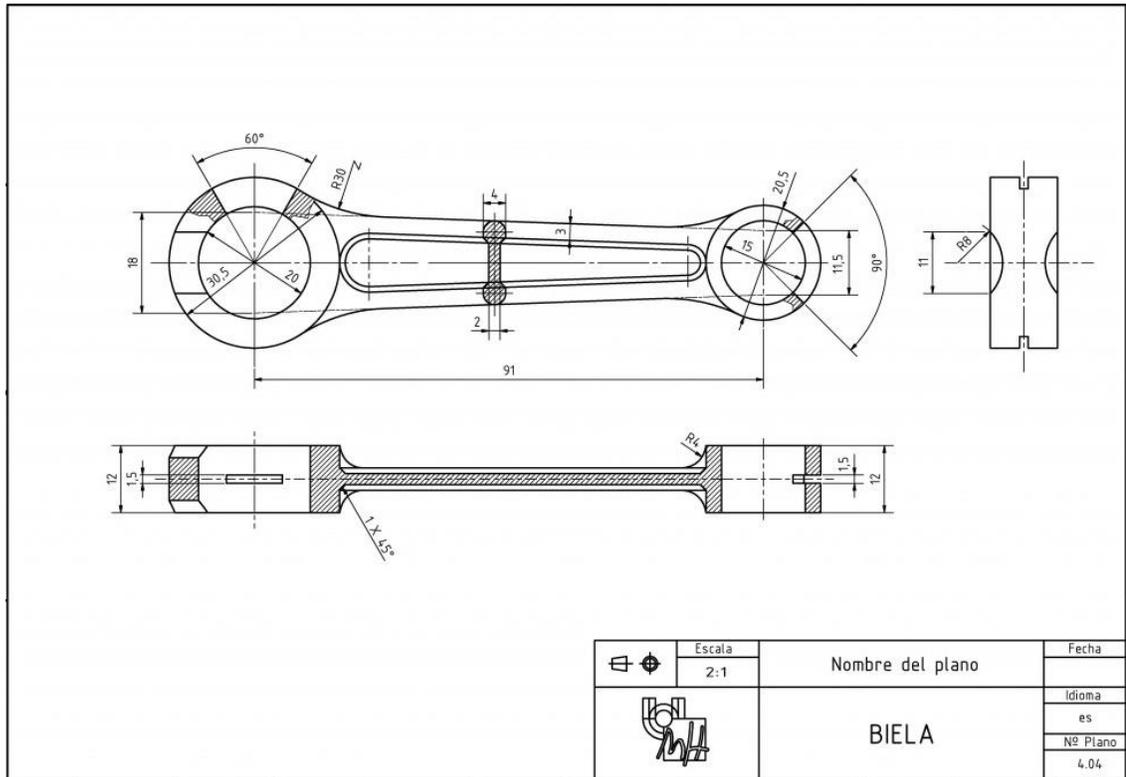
Plano de fabricación (Fuente: dibujotecnico.edu.umh.es)
